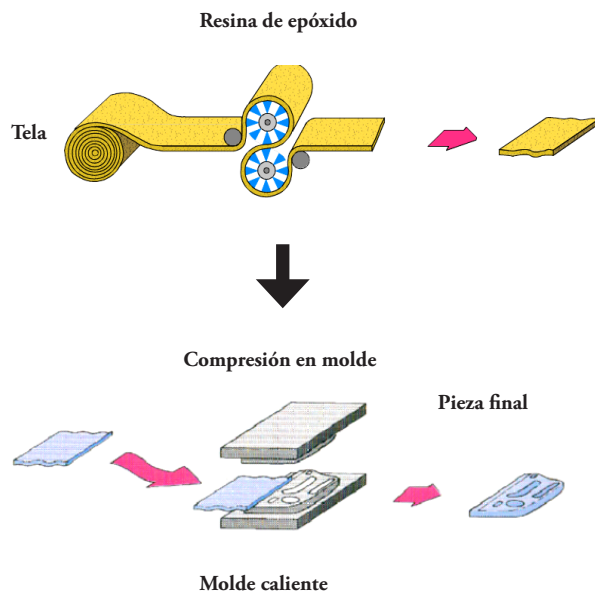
Moldeo por compresión: NF-EP (BMW 5-Series – Johnson Controls)
